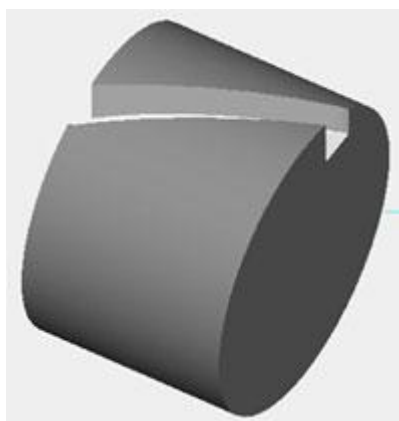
Необхідно отримати гвинтову канавку на поверхні вала. Вал закріплений в кулачках керованого поворотного столу. Найпростіший спосіб обробки такої канавки – розрахунок за допомогою CAD / CAM-системи
